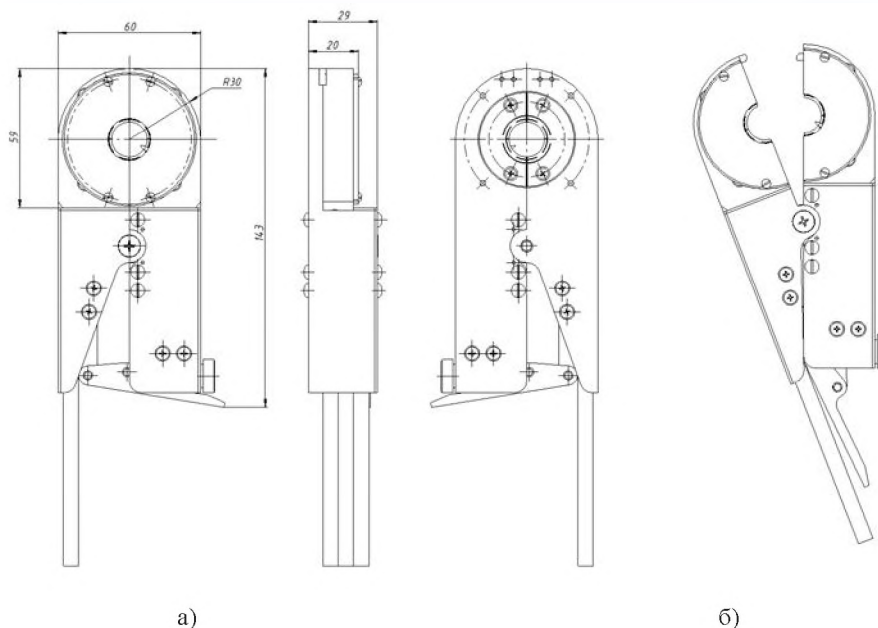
Эскиз малогабаритной камерной сварочной головки с габаритными размерами в открытом (а) и закрытом (б) состоянии
